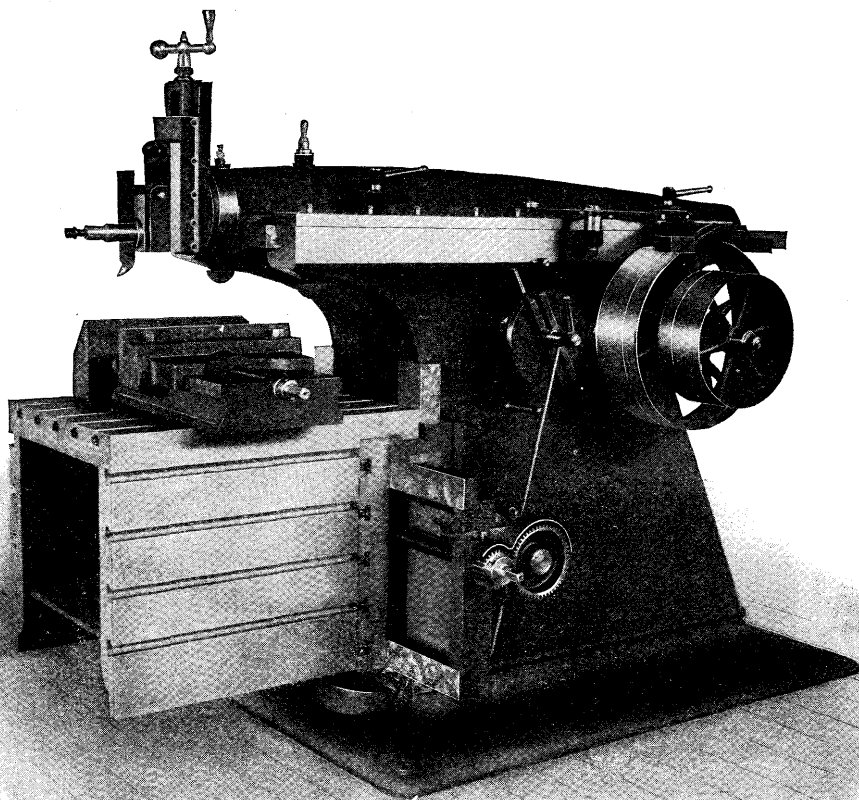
Etai-limeur de MM. Geo. Walcott et fils.
